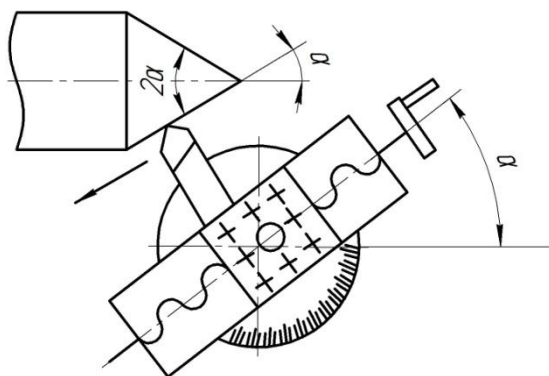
Обробка конічної поверхні поворотом ползків верхнього супорта
